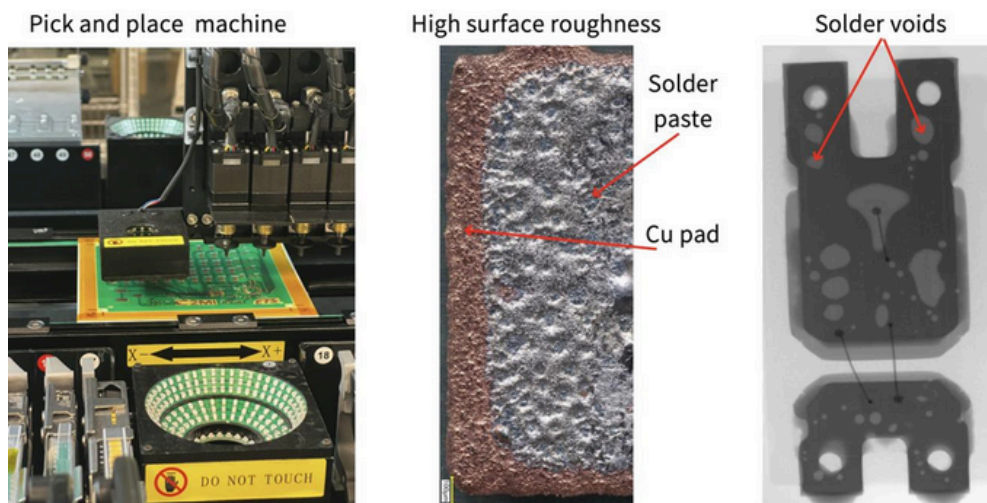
Placement des composants par pick-and-place et analyse de soudure.
